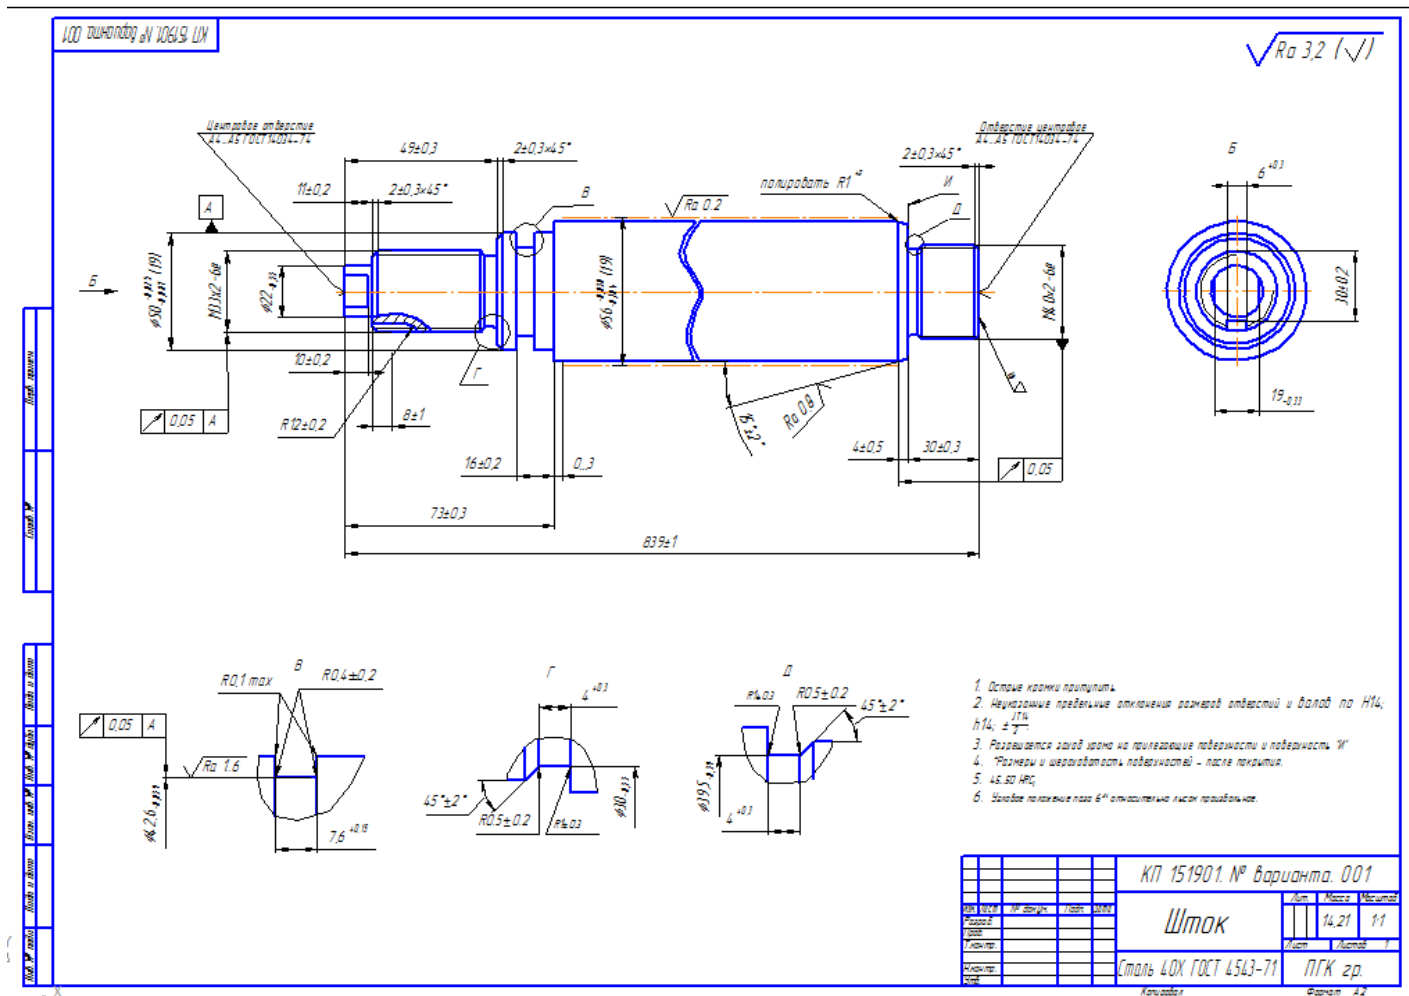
Рабочий чертеж детали «Шток».
